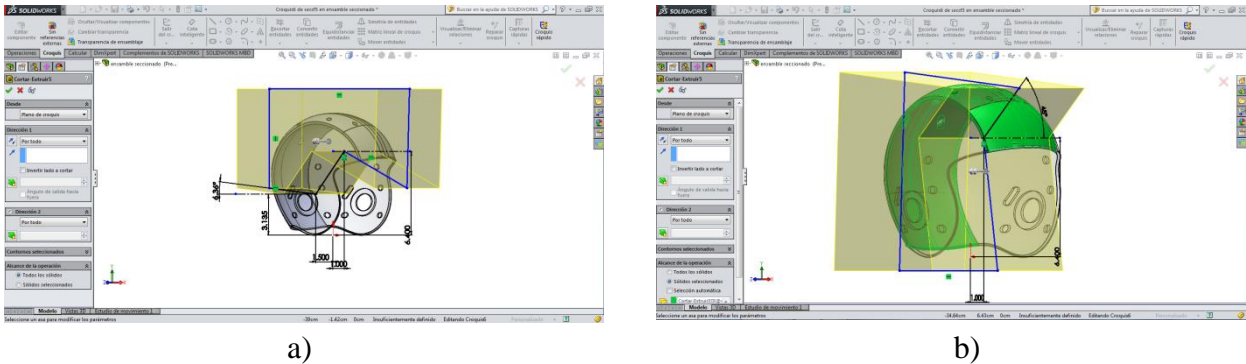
Partes seccionadas. a) Parte trasera del casco. b) Parte frontal del casco.
